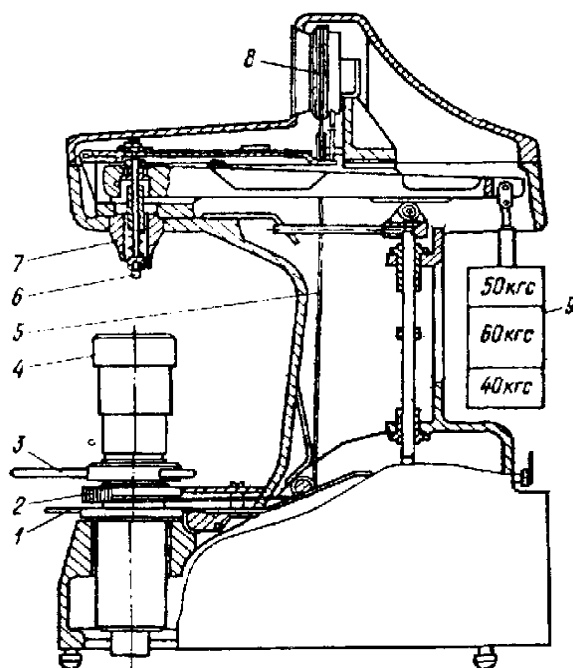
Схема прибора измерению твердости по Роквеллу
